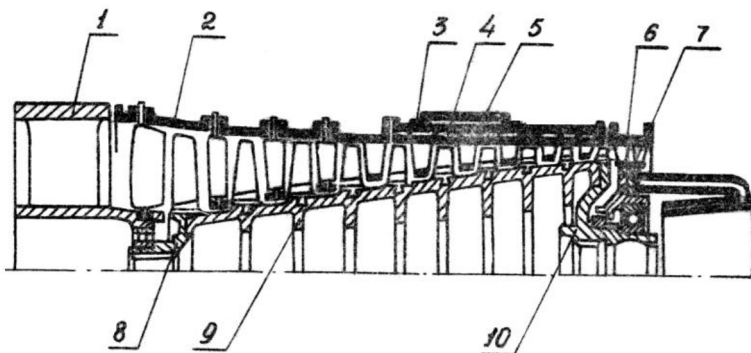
Схема компрессора: 1 – передняя опора; 2 – передний корпус компрессора; 3 – средний корпус; 4 – промежуточное кольцо; 5 – спрямляющий аппарат; 6 – задний корпус компрессора; 7 – задняя опора; 8 – диск I – ступени ротора; 9 – барабан ротора; 10 – диск X –й ступени ротора
